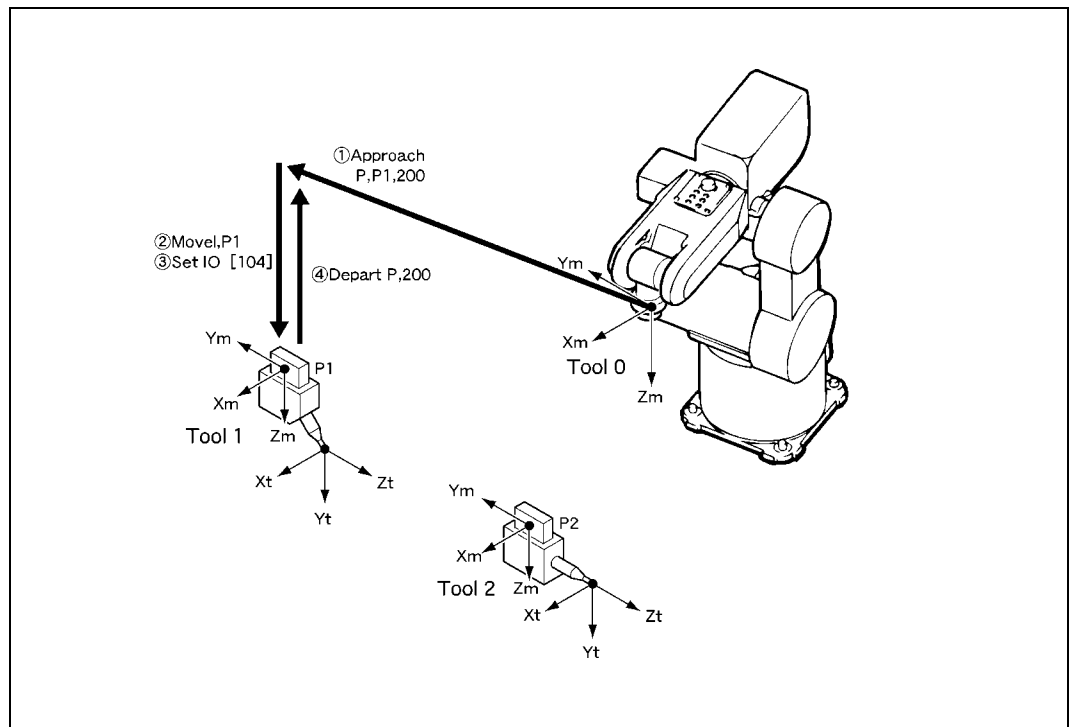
Verfahrenweg zum Einstellen von Endwerkzeug 1
